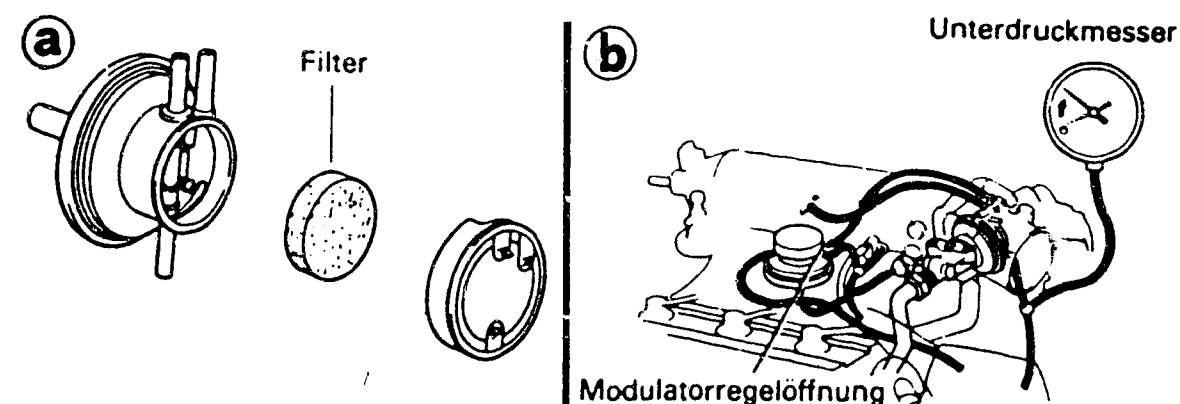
Motor 4A-GE mit Abgasrückführung. a) Die Filter im Modulator lassen sich mit Druckluft reinigen. – b) Anschluss des Unterdruckmanometers zwischen Modulator und EGR-Ventil.
